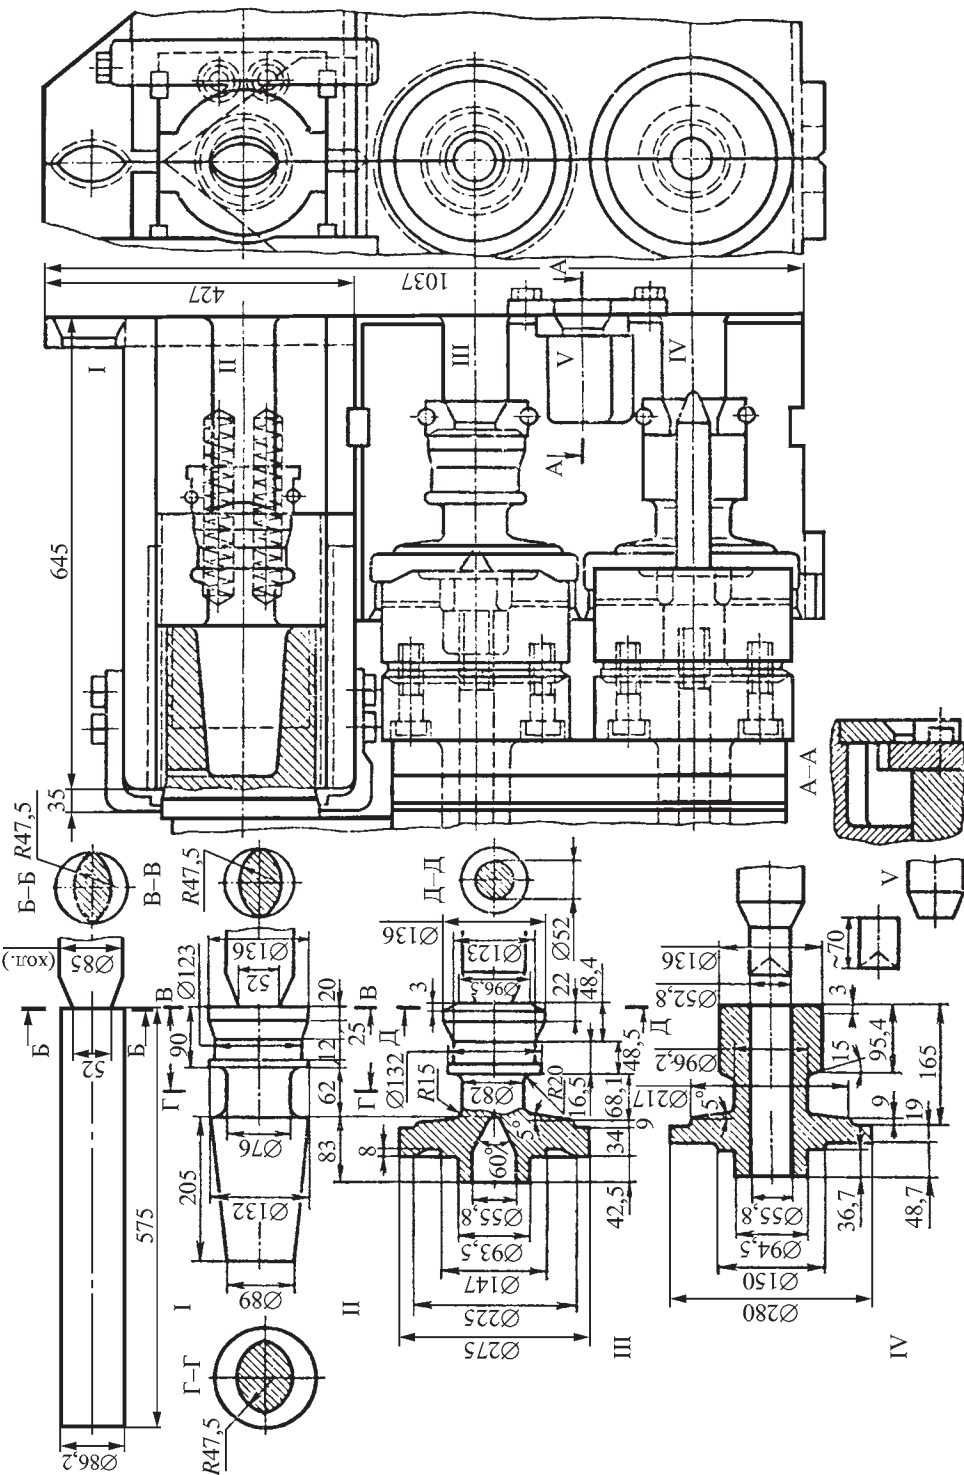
Штамп со скользящими матрицами для изготовления поковки цилиндрической шестерни и переходы штамповки
